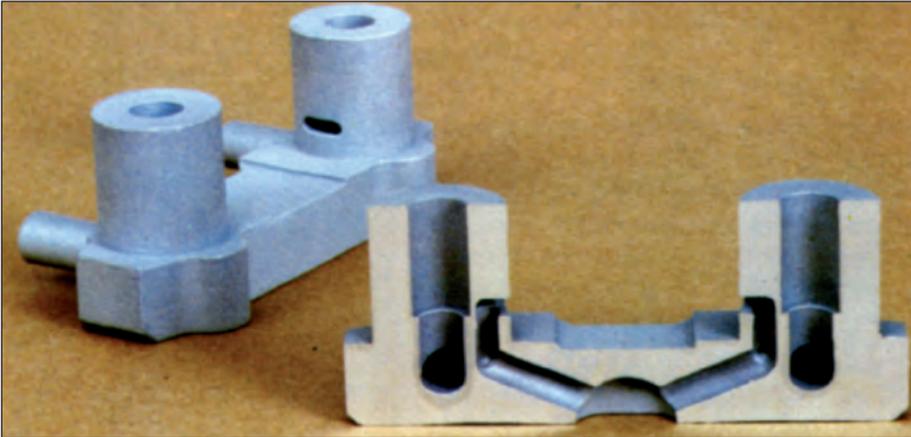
Ansicht und Schnitt durch einen Saugkörper für ein hydraulisches Aggregat aus dem Werkstoff EN-AC-AISi7Mg0,3 (W.-Nr. EN AC-42100), Abmessungen: 77 x 35 x 34 mm, Gewicht: 70 g, dessen eng dimensionierte Innenkonturen mit einem keramischen Kern ausgebildet werden. (Bild: Feinguss Blank, Riedlingen)
